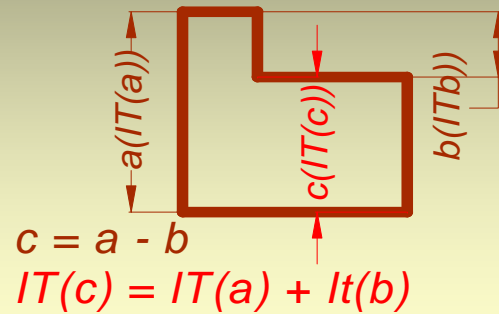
Схема формування похибки позиціонування заготовки при неспівпадінні технологічних баз: установочної (А) та вимірної (В)
